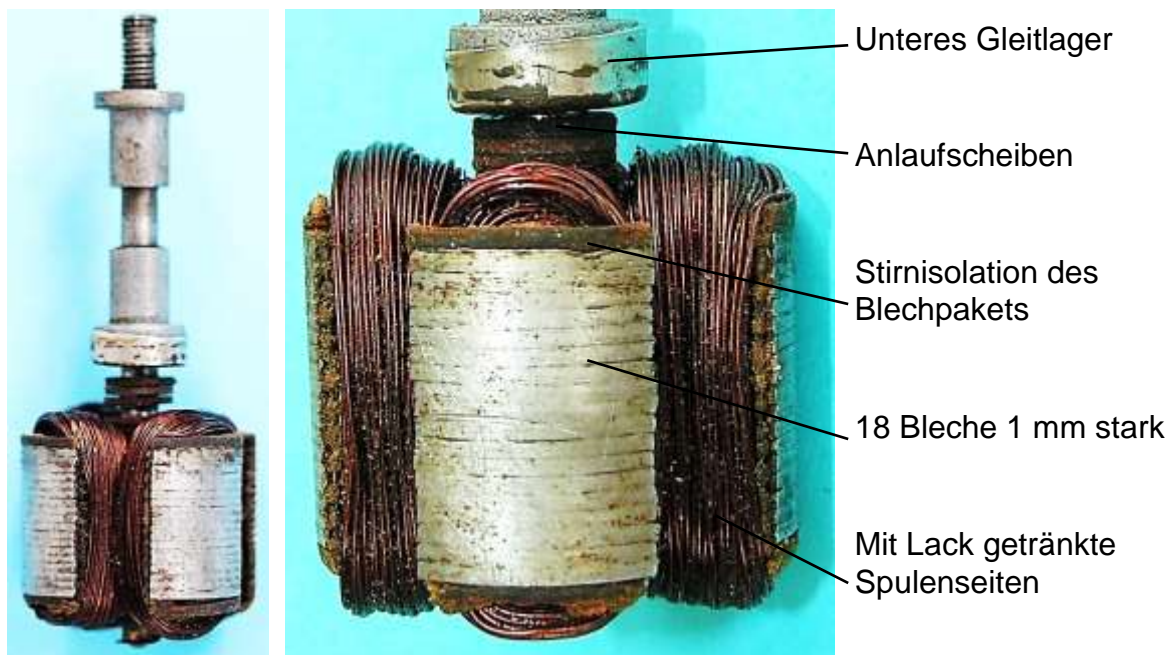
Anker: Durchmesser: 31,5:mm, Blechpaketlänge 19 mm
